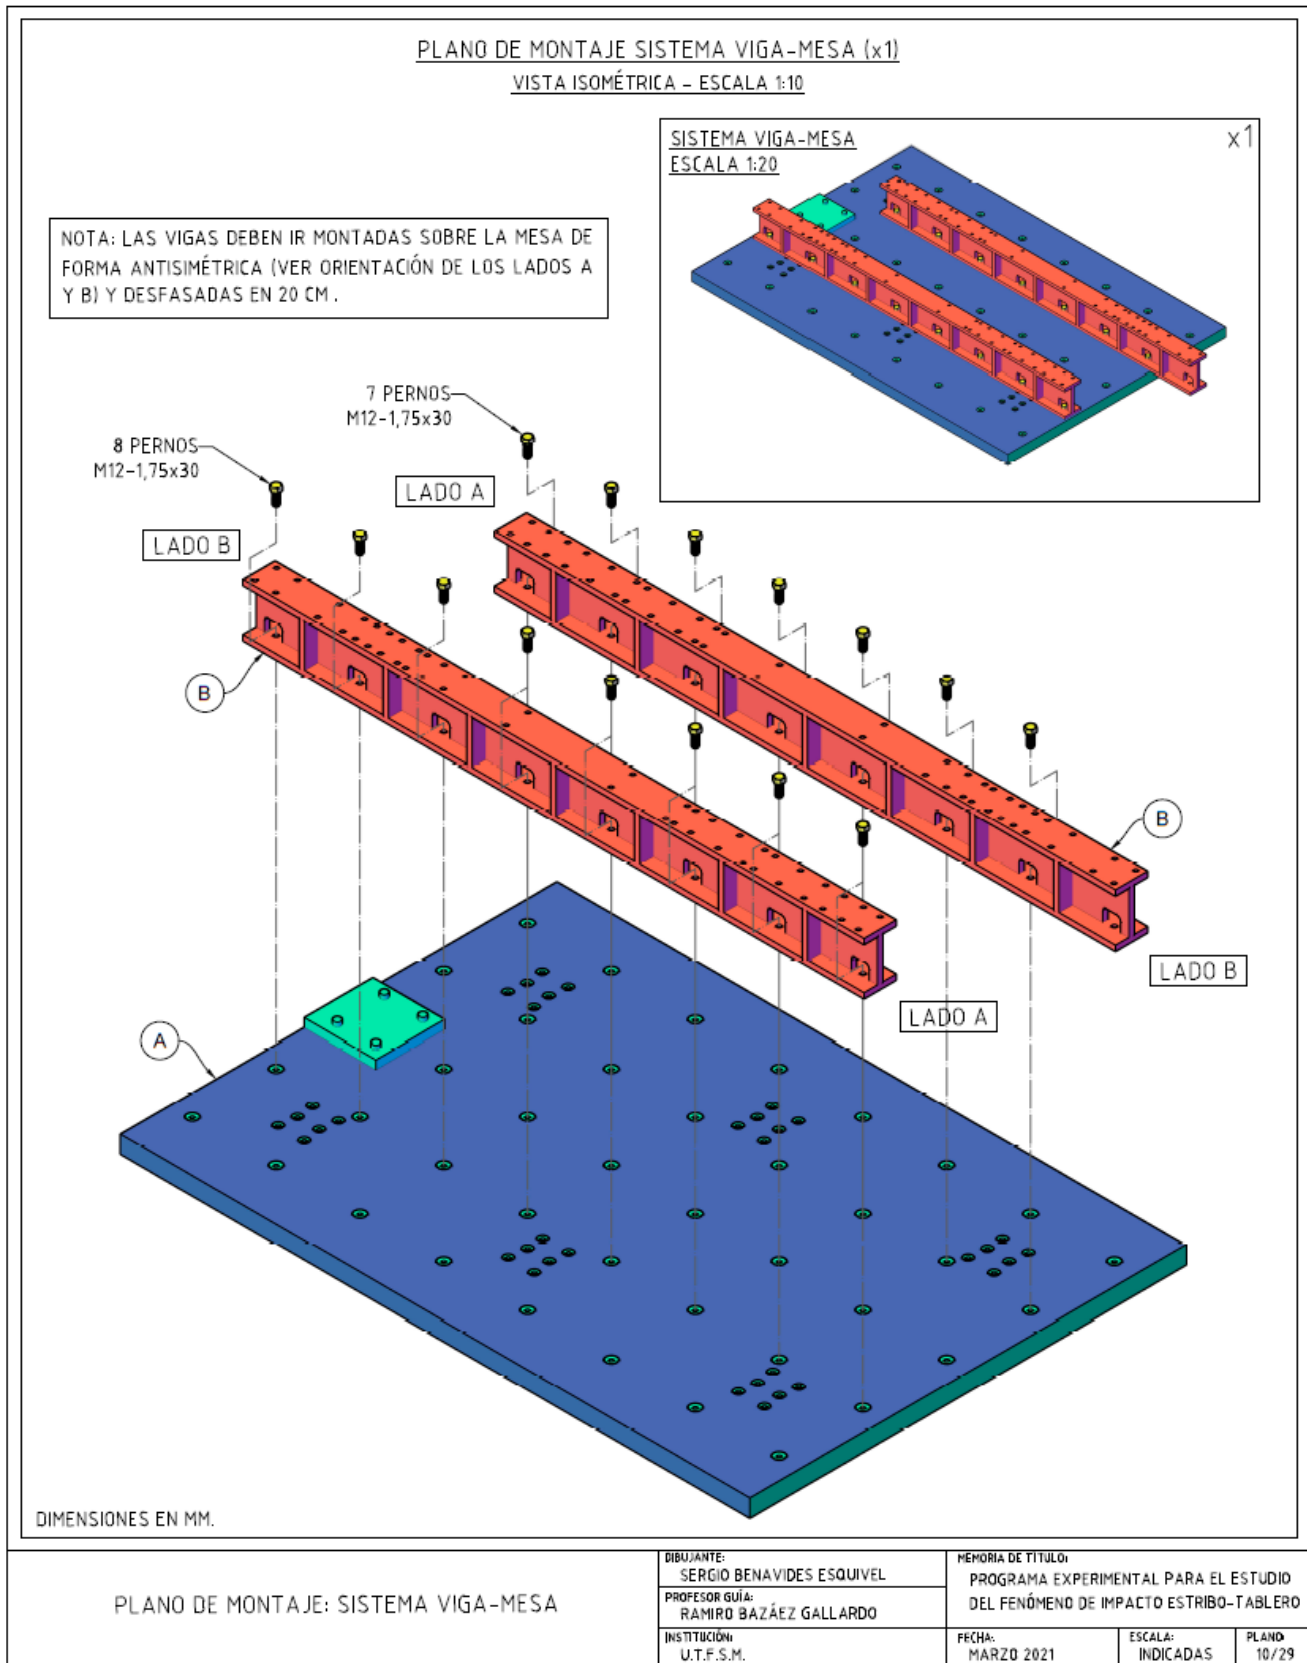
Plano de Montaje: Sistema Viga-Mesa.
